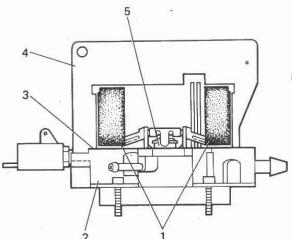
Instalación del nivel de combustible en la cuba del carburador 21053-1107010: 1 - flotador; 2 - tapa del carburador; 3 - junta;
